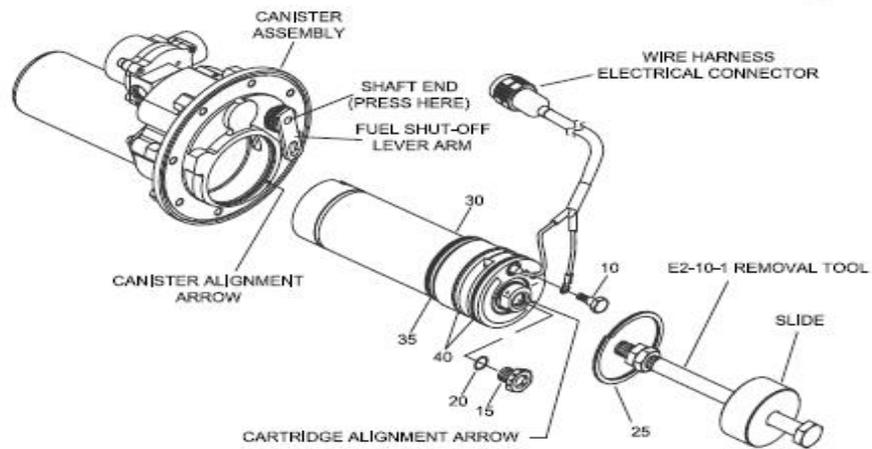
Bomba Auxiliar DC Removable (A)
